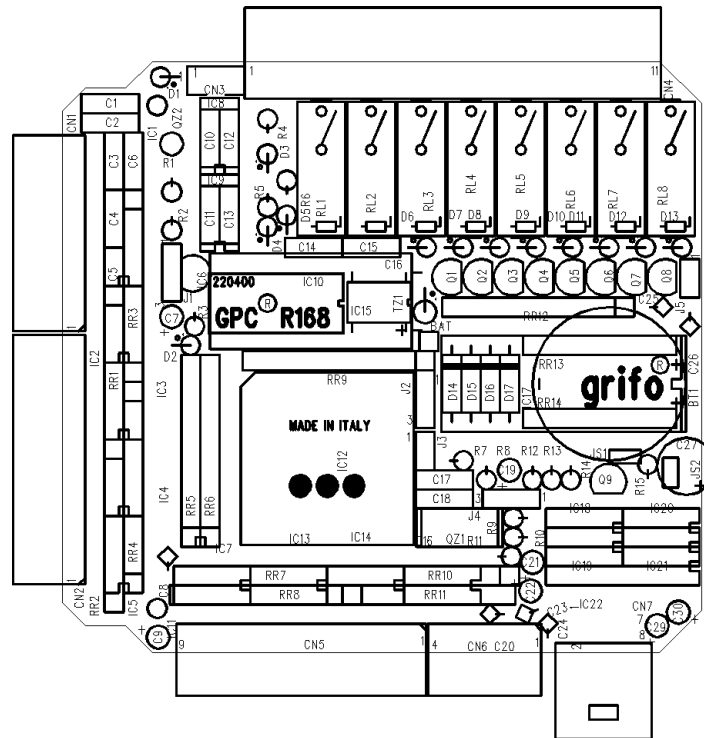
PIANTA COMPONENTI GPC® R168 (LATO SALDATURA)
